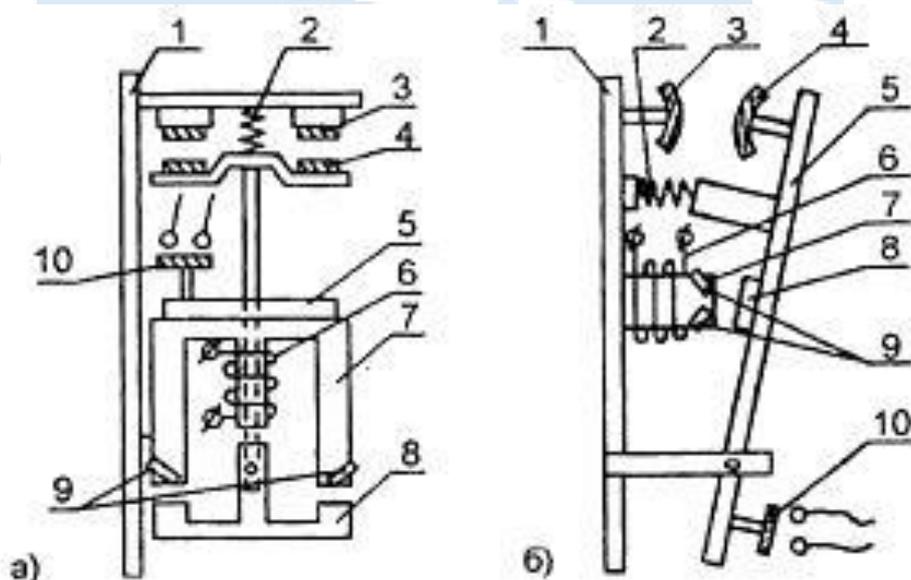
Устройство магнитных пускателей с прямоходовой Ш-образной (а) и поворотной-рычажной П-образной (б) магнитными схемами:
